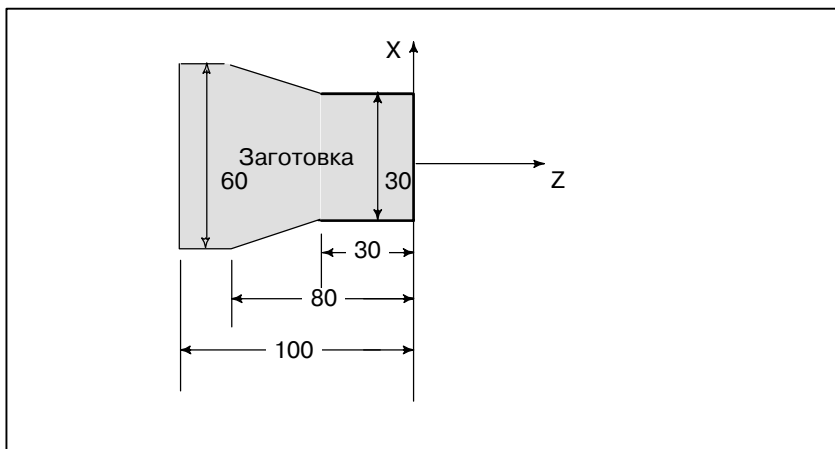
(е) Координаты и размеры на чертеже детали
